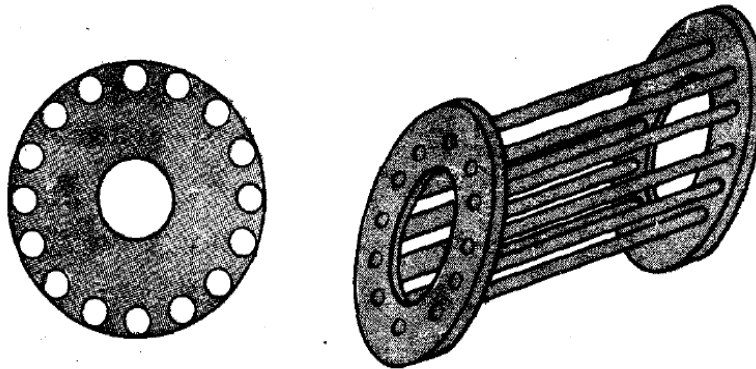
Rotor de un motor de jaula de ardilla [1]
